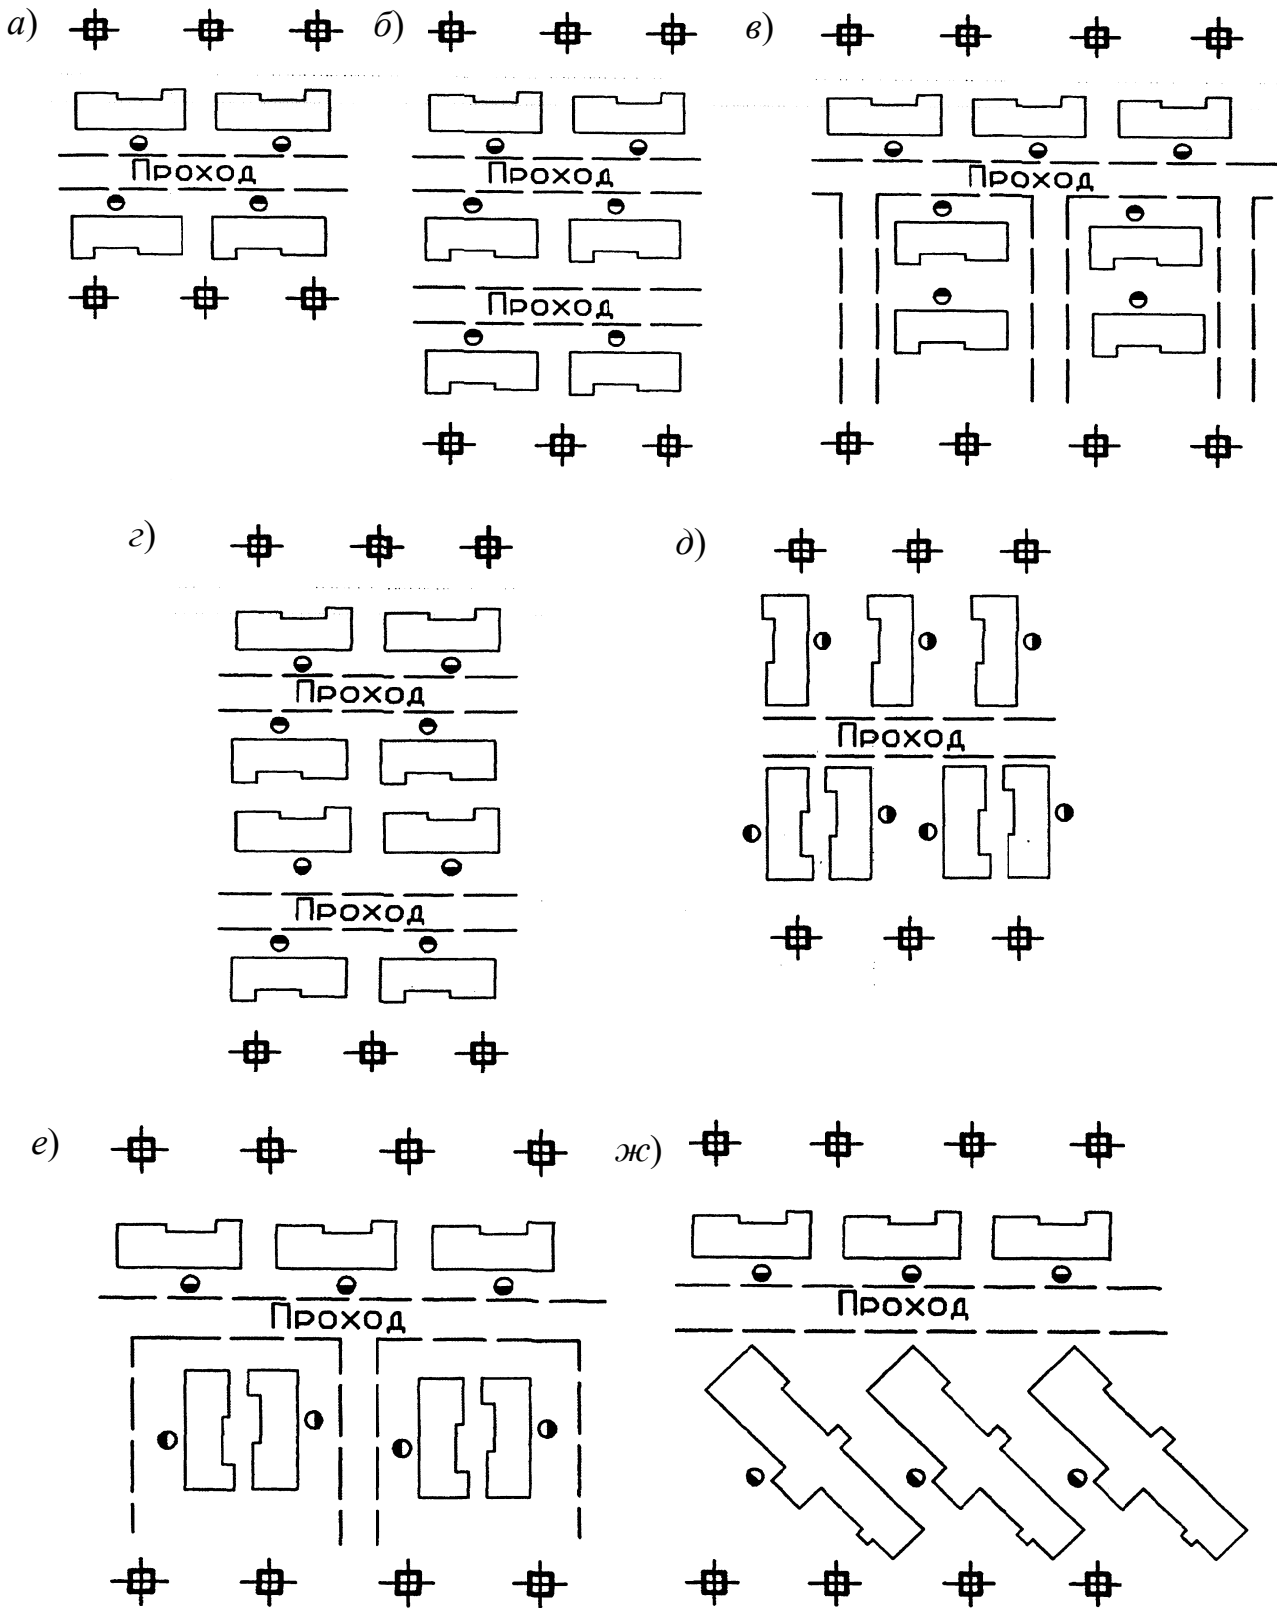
Типовые схемы расположения металлорежущих станков в пролете цеха
